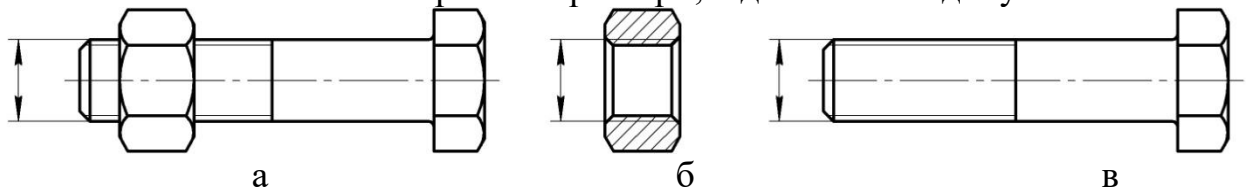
а – ескізи різьбового з'єднання; б – деталь з внутрішньою різзю; в – деталь з зовнішньою різзю
